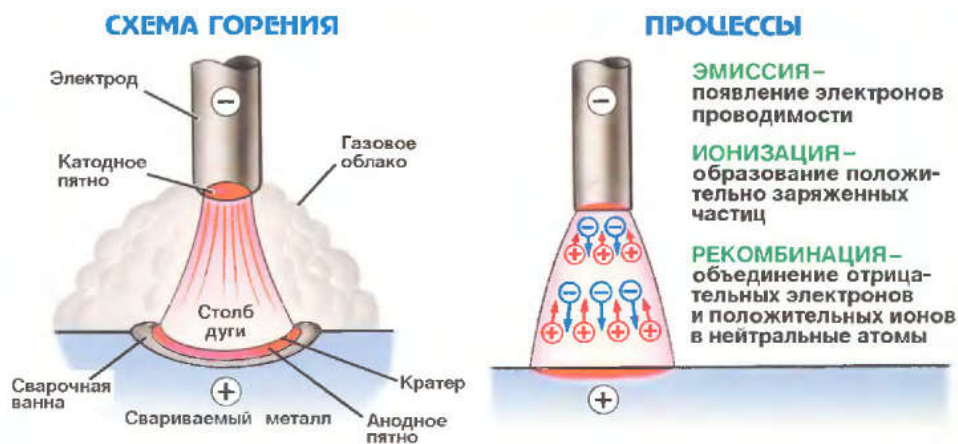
Процессы, возникающие при создании сварного соединения
